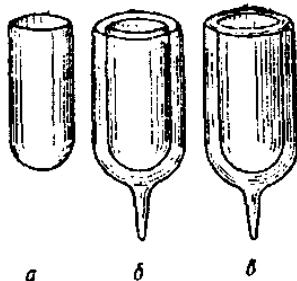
Изготовление дьюаровского спаев приемом закатывания наружного цилиндра на внутренний:
